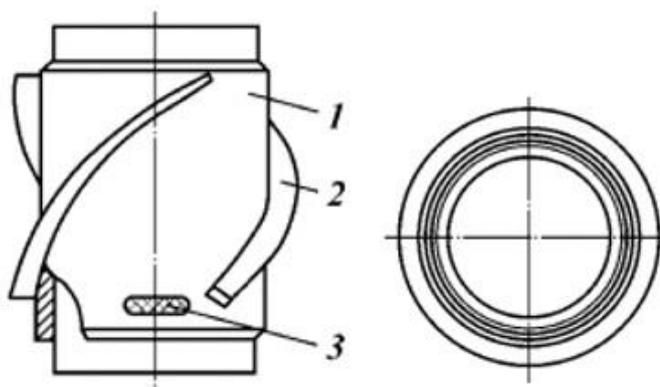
Турбулизатор: 1 – корпус; 2 – лопасти; 3 – винтовой клин-стопор
